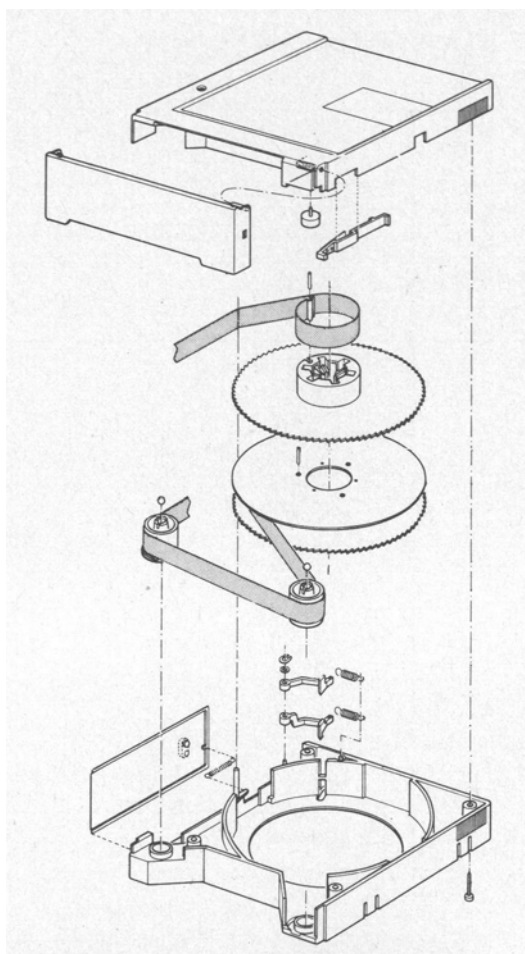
Explosionsansicht einer VCR-Kassette [17]
